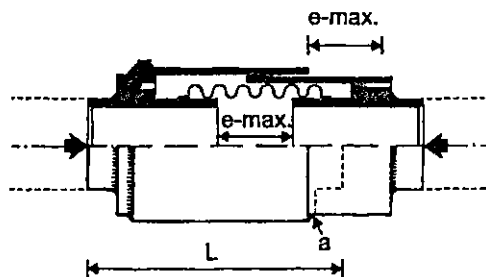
E-компенсатор Буквой "а" показано место сварки кожуха компенсатора после его сжатия
